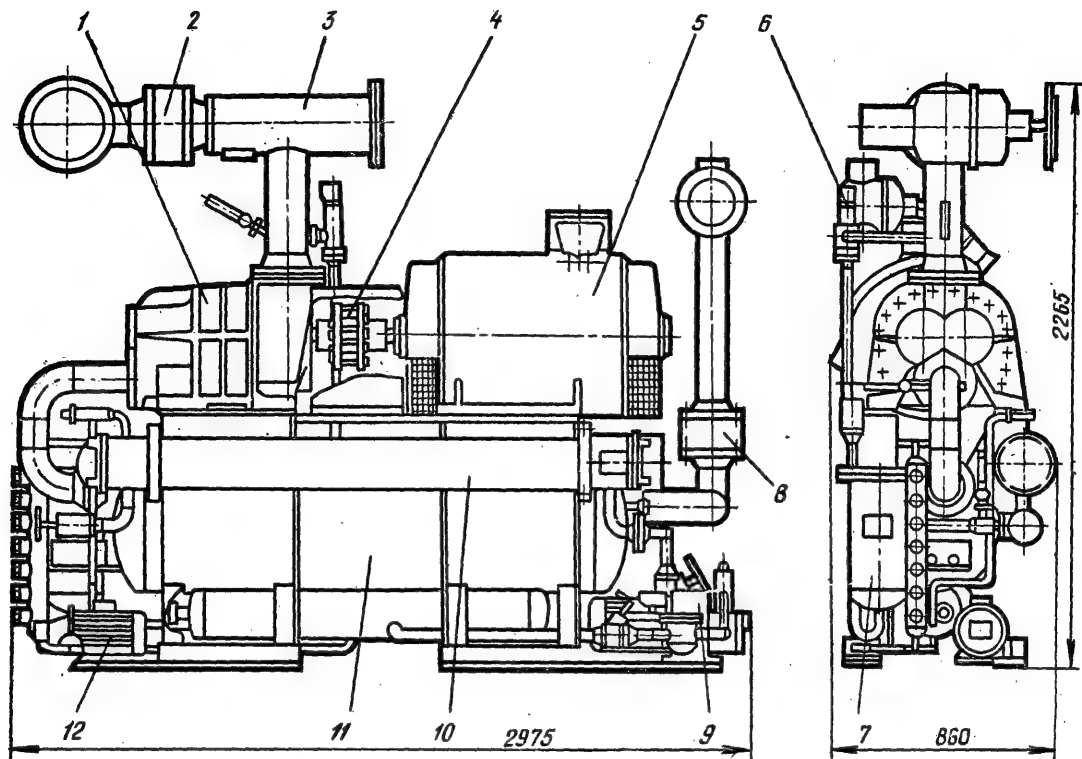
Винтовой компрессорный агрегат S3-900 (ГДР):
